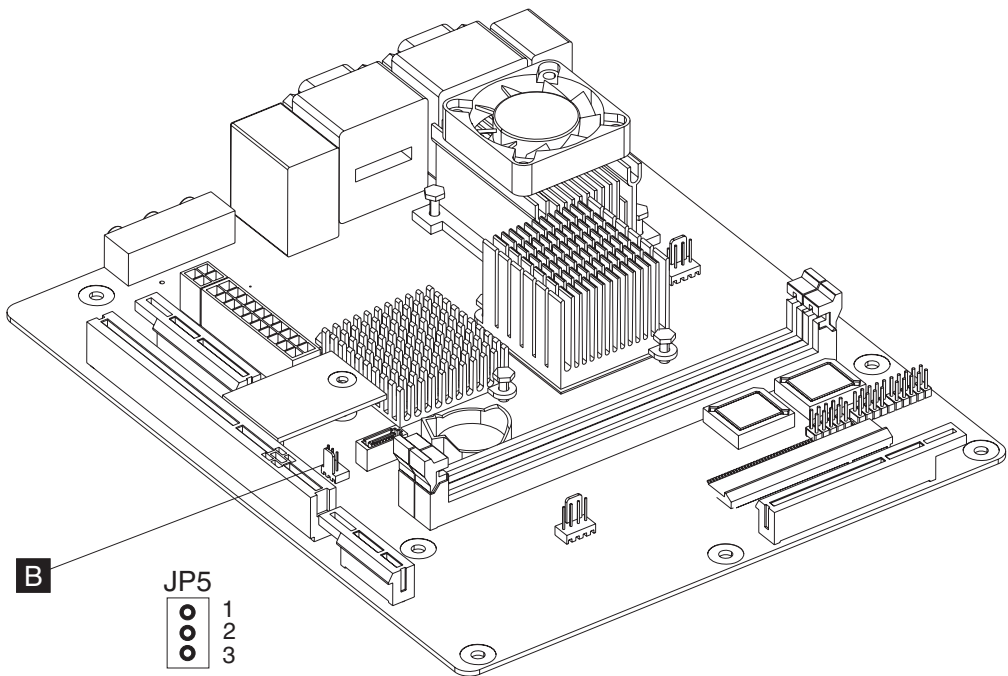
CMOS 跳线的位置 - 型号 723 和 E23
